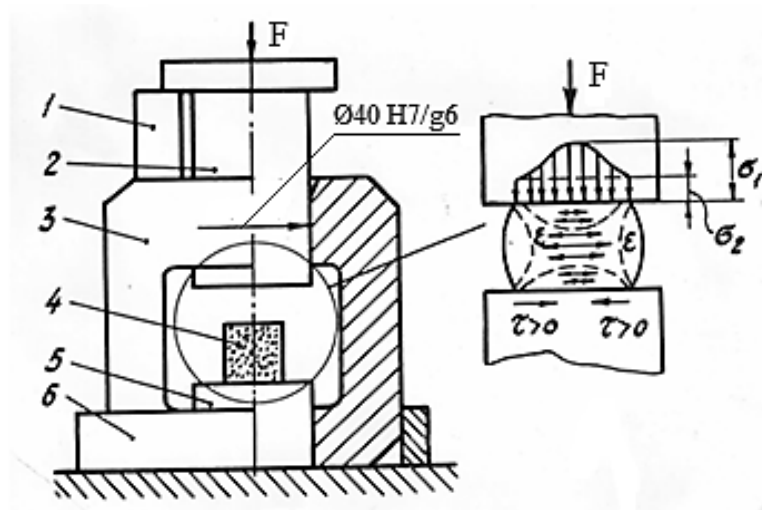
Приспособление для осадки цилиндрических образцов:
